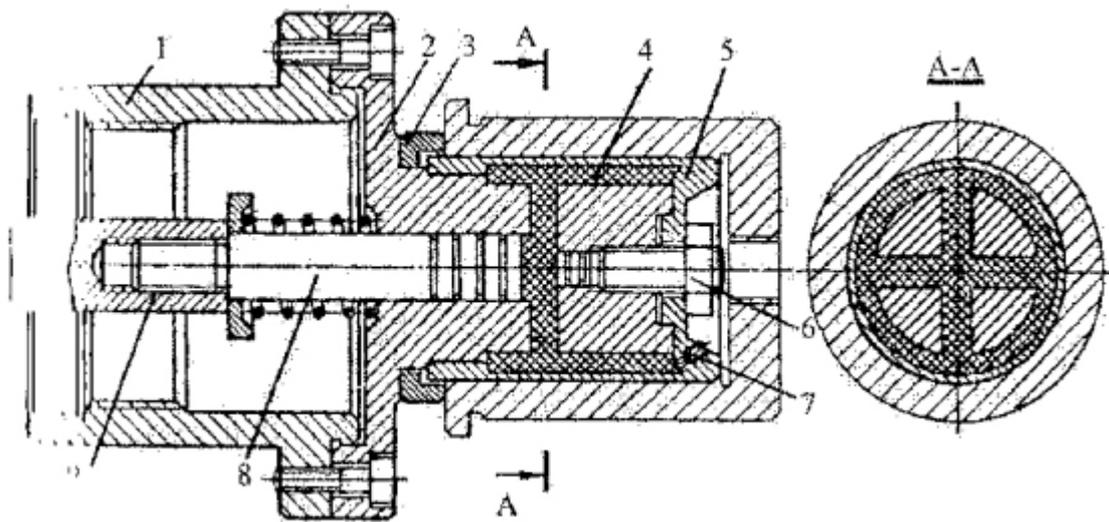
Конструкция пневматической оправки с гидропластом.
